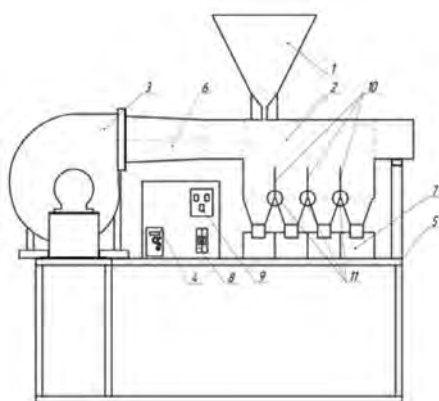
Пневматический сепаратор (расшифровка обозначений в тексте)
